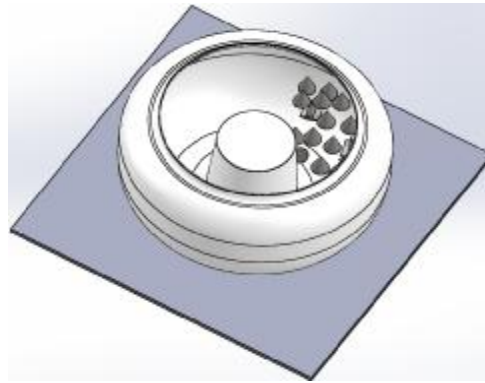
Detalle diseño vibro con moletas y piezas de zámak.
